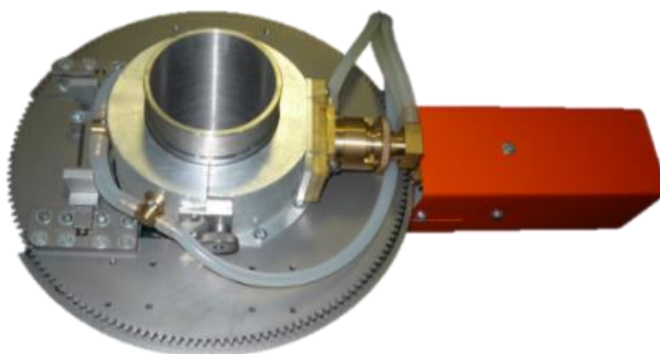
Сварочная головка ГНС 70-105
